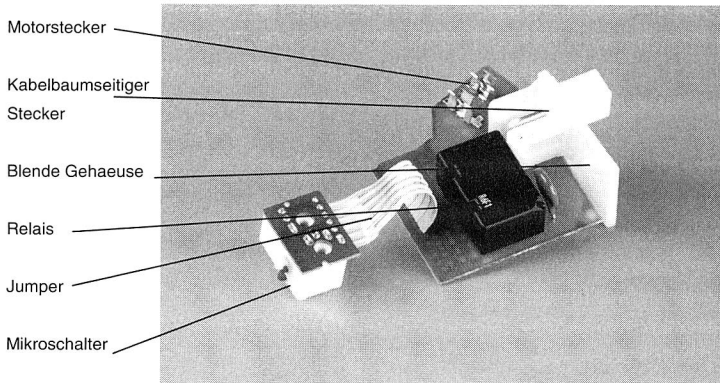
Schiebedachsteuerung in konventioneller Aufbautechnik
